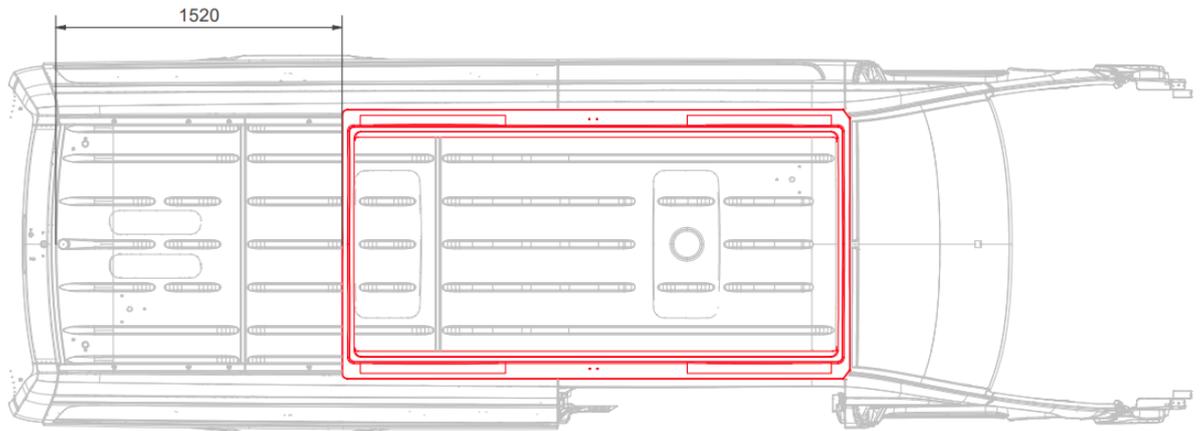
MB Sprinter L2H2 (L = 6967 mm) [G0002136]
